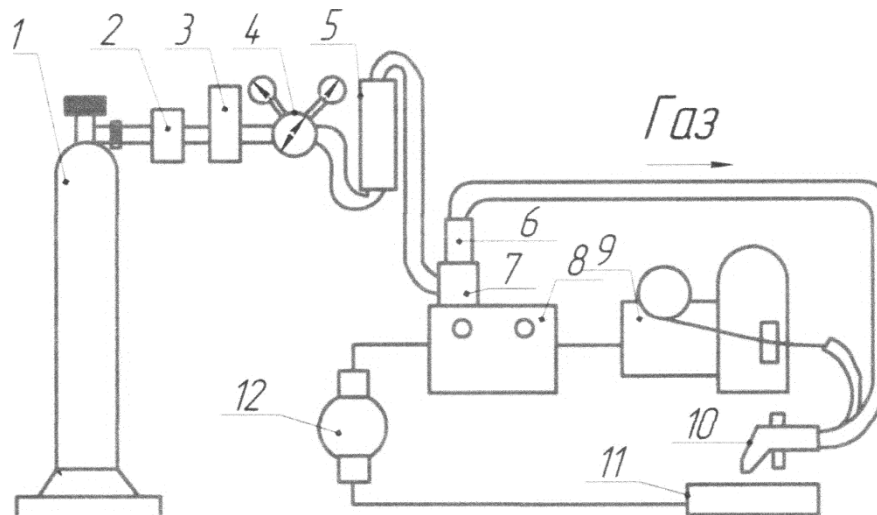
Схема установки для наплавлення в середовищі CO₂: 1 - балон з вуглекислим газом; 2 - осушувач; 3 - підігрівач газу; 4 - газовий редуктор; 5 - витратомір газу; 6 - клапан; 7 - електромагніт; 8 - апаратний ящик; 9 - механізм подачі дроту; 10 - пальник; 11 - відновлююча деталь; 12 - джерело струму». ^{iv}
